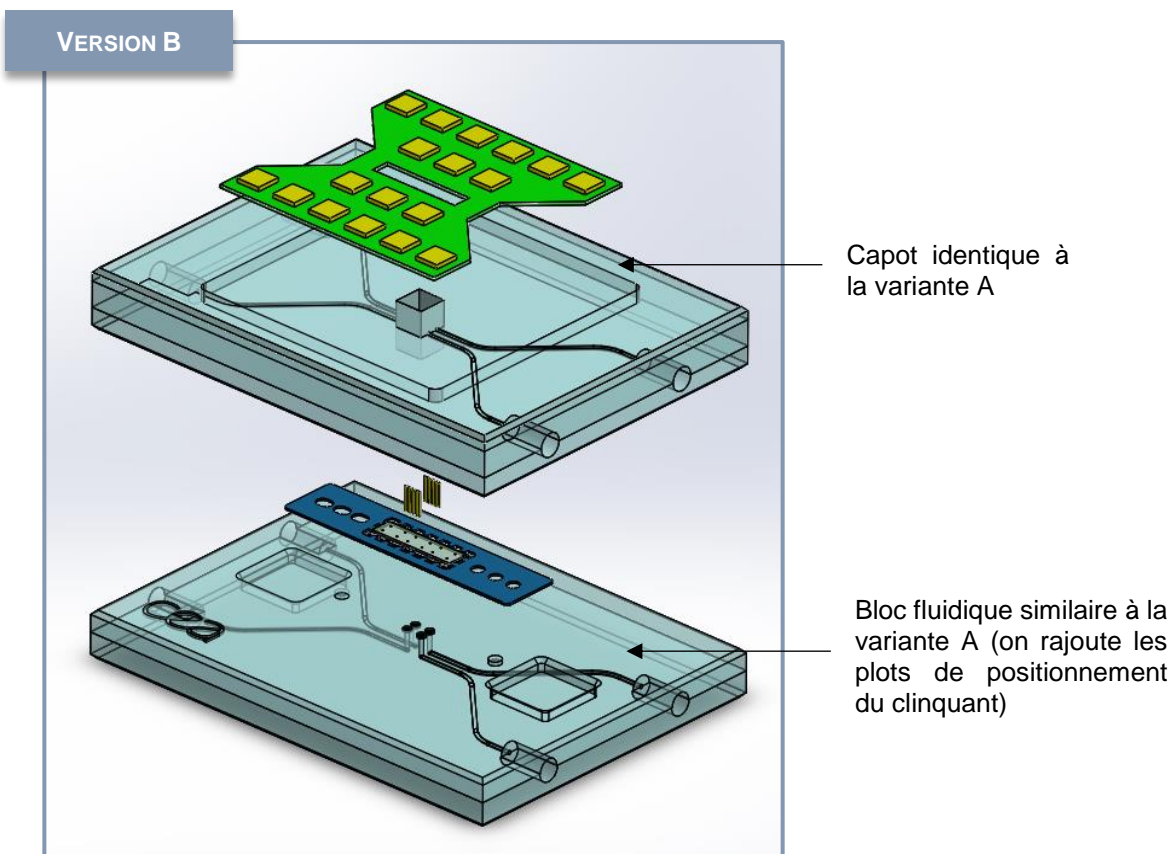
Vue éclatée de la variante B « fluidique face arrière » de la plateforme
